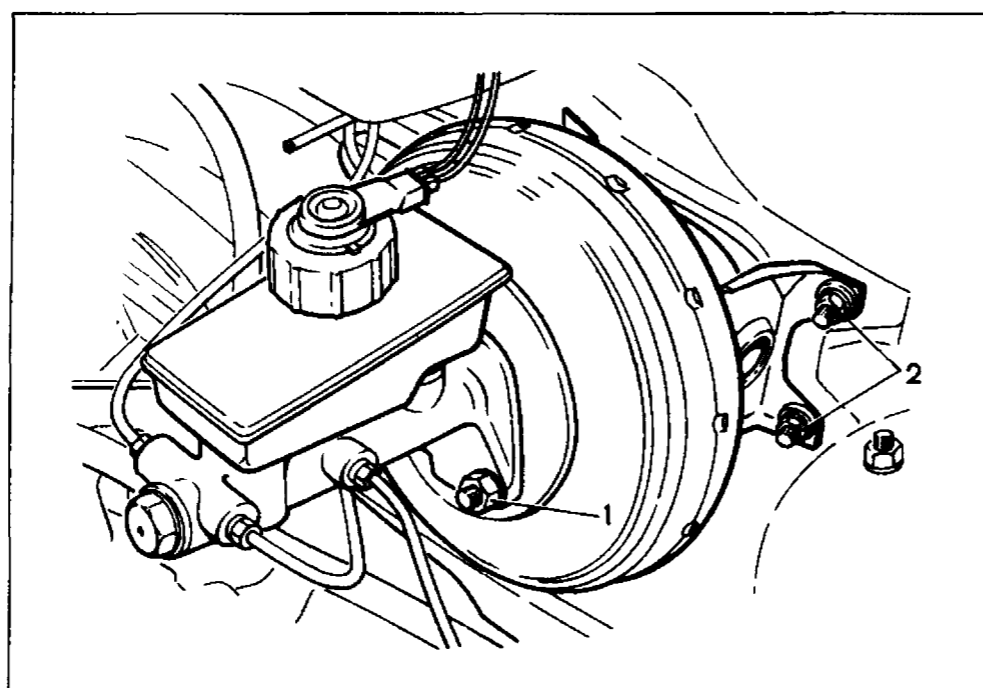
Крепление вакуумного усилителя и главного цилиндра: 1 — гайка крепления главного цилиндра; 2 — гайка крепления кронштейна вакуумного усилителя
